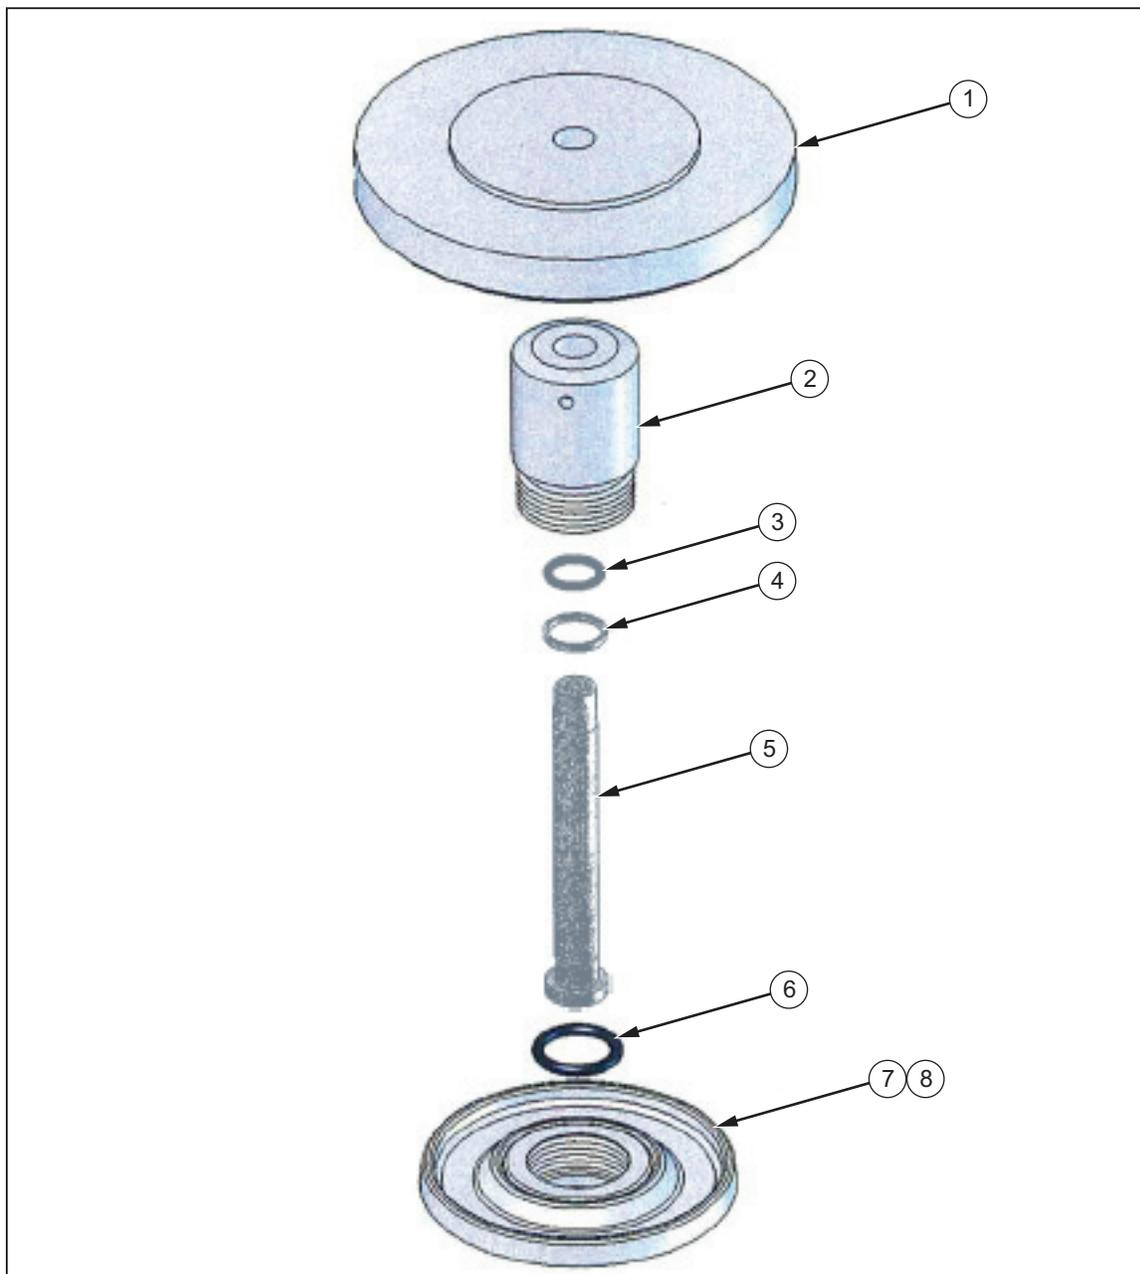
Сборочный чертеж поршневой пары - 10 мм
